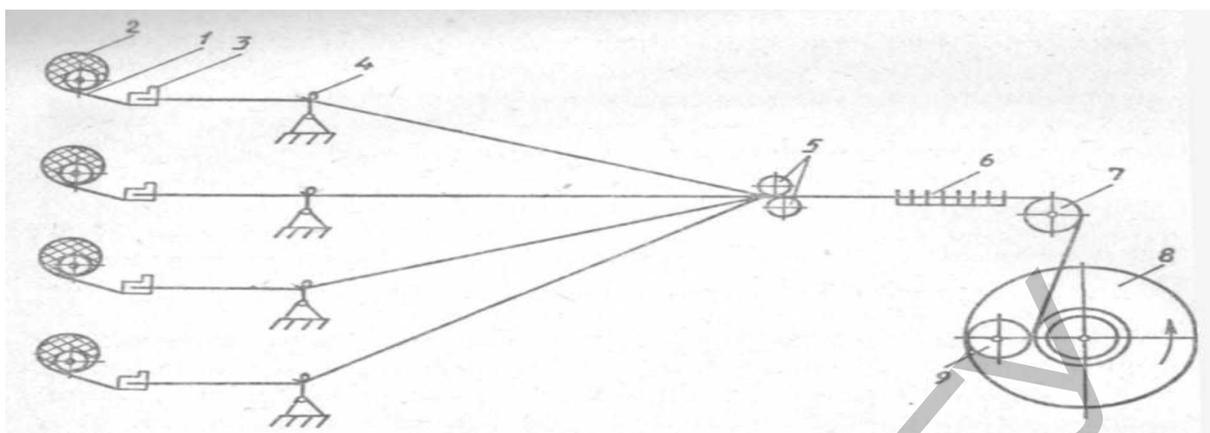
Схема заправки партионной сновальной машины: 1 — сматываемая нить; 2 — бобина; 3 — натяжное устройство; 4 — крючок электроостанова при обрыве нити; 5 — направляющие прутки; 6 — рядок; 7 — мерильный валик; 8 — сновальный вал; 9 — укатывающий валик
